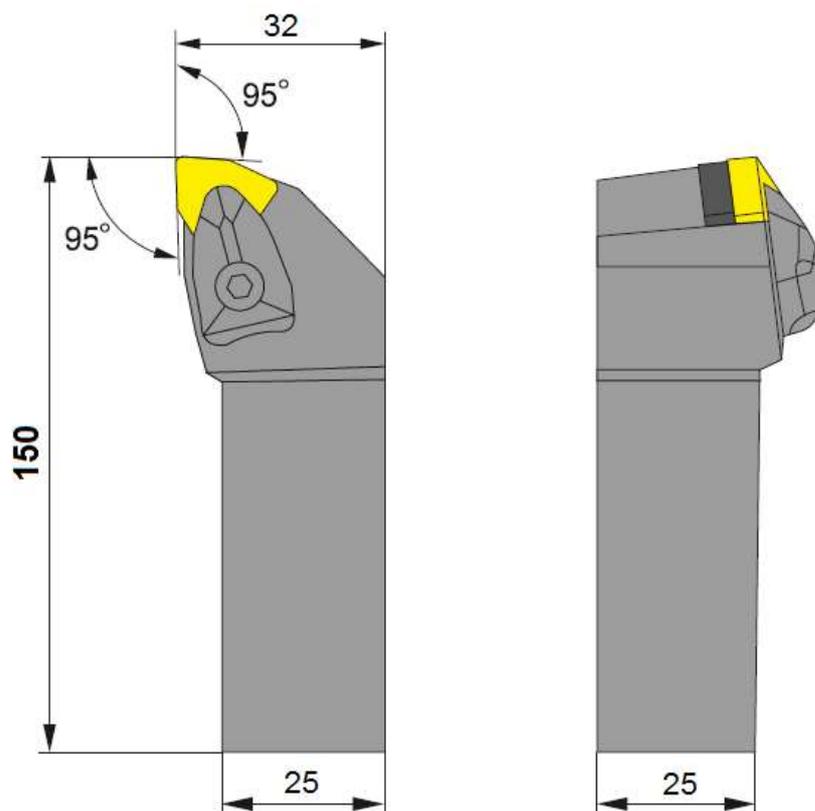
Резец DWLNR 2525 M06-04
